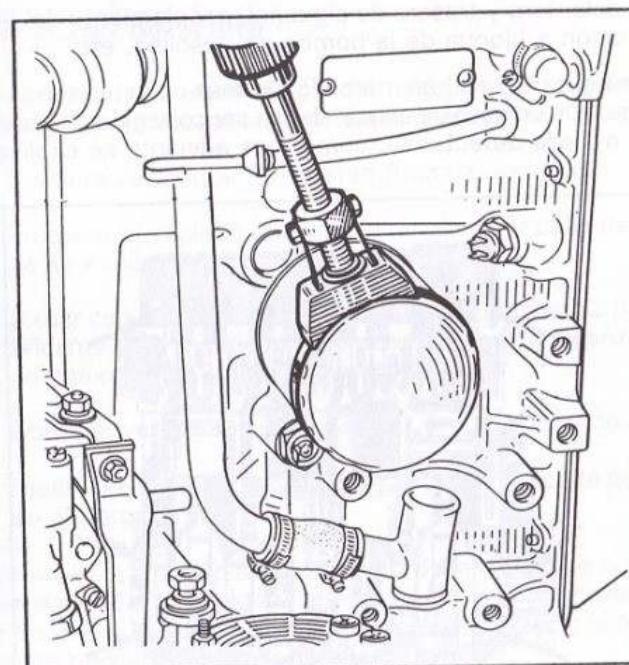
Util para el desmontaje del filtro del aceite.
